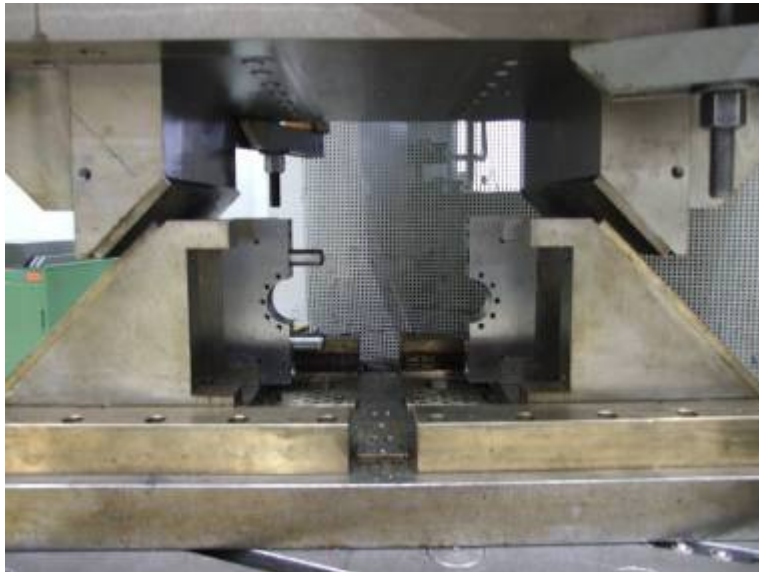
Rollbiegewerkzeug bei der Einarbeitung
